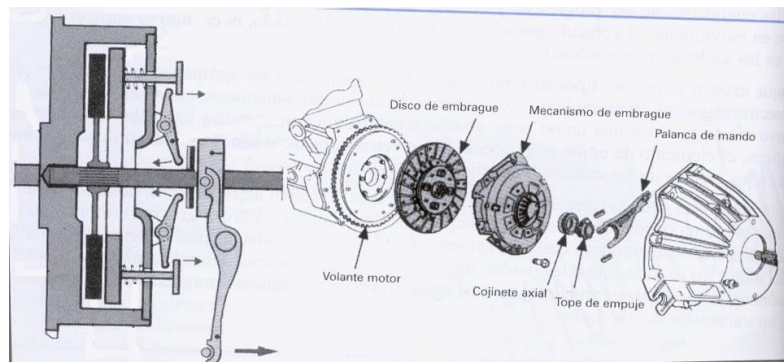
Despiece de los componentes del Sistema de Embrague
